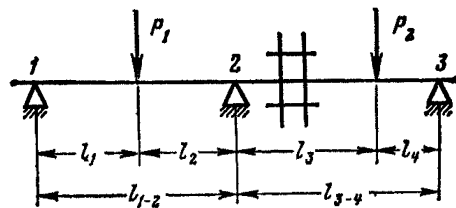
Определение нагрузок на подшипники трехопорного вала
